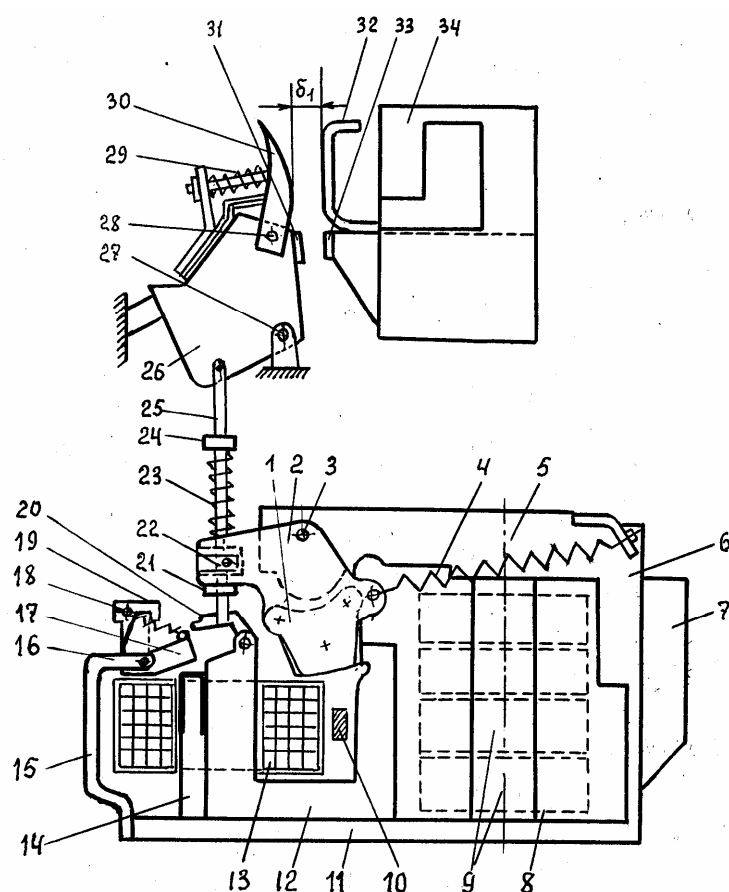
Электромагнитный механизм и блок главных контактов выключателя ВАБ-43: 1 – подвижный якорь; 2 – боковины; 3,16,22,27,28 – оси; 4 – отключающая пружина; 5 – верхний брус; 6 – основание; 7 – регулировочная планка; 8 – сердечник; 9 – держащая катушка; 10 – шина; 11 – нижний брус; 12 – магнитопровод; 13 – катушка управления; 14 – сердечник механизма свободного расцепления; 15 – скоба; 17 – якорь; 18,29 – пружина; 19 – защёлка; 20 – рычаг; 21,24 – упор; 23 – пружина поджатия; 25 – тяга; 26 – подвижный контакт; 29,30,32 – дугогасительные контакты; 31,33 – серебряные наконечники контактов; 34 – неподвижный контакт
